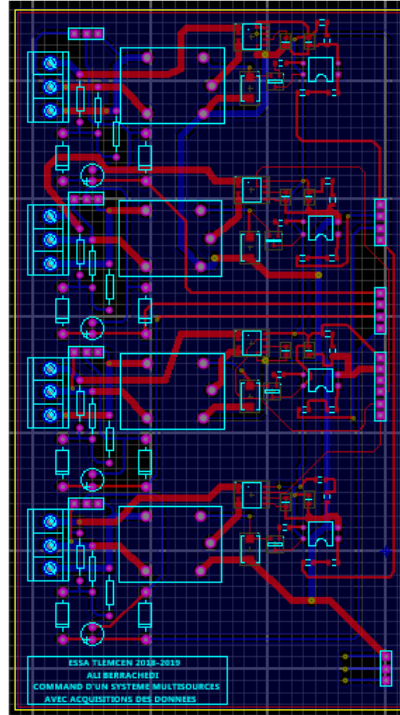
PCB de la carte sous Isis Proteus V8.
